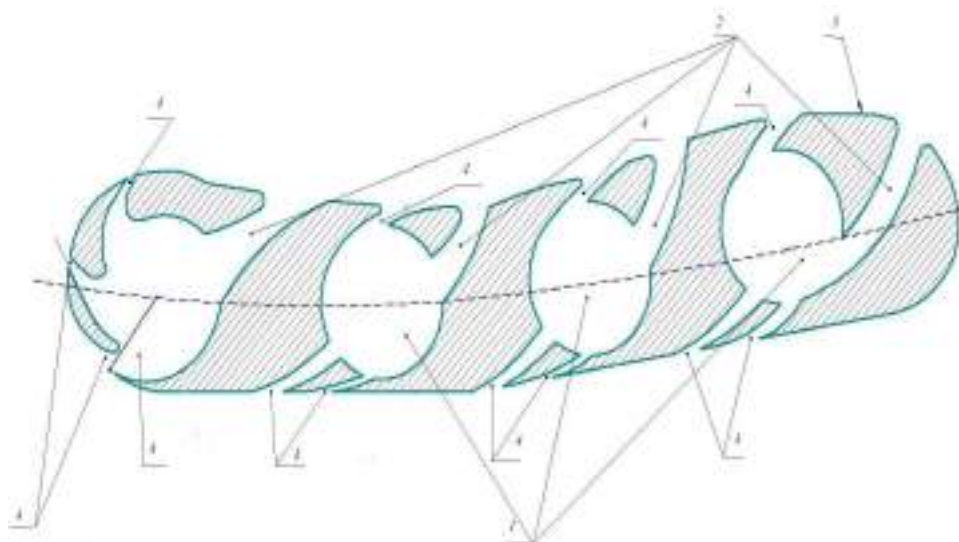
Лопатка рабочего колеса газоотсасывающего шахтного вентилятора с вихревыми камерами
